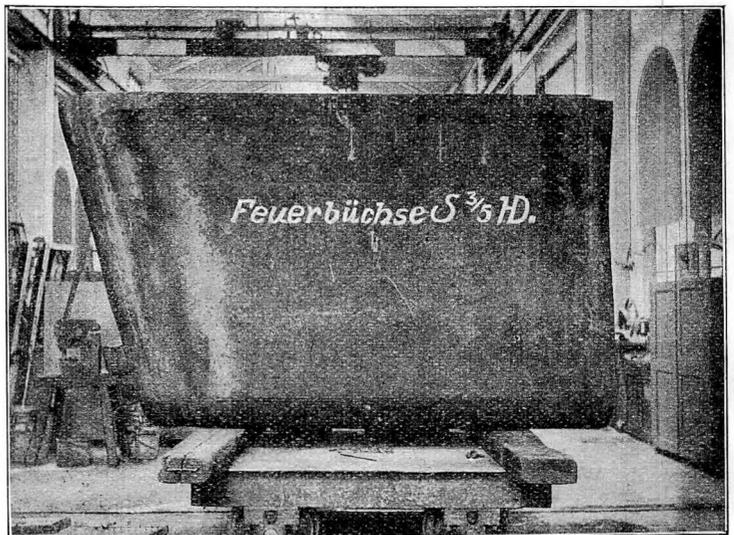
Fertig geschweißte Feuerbüchse. Außenansicht.
